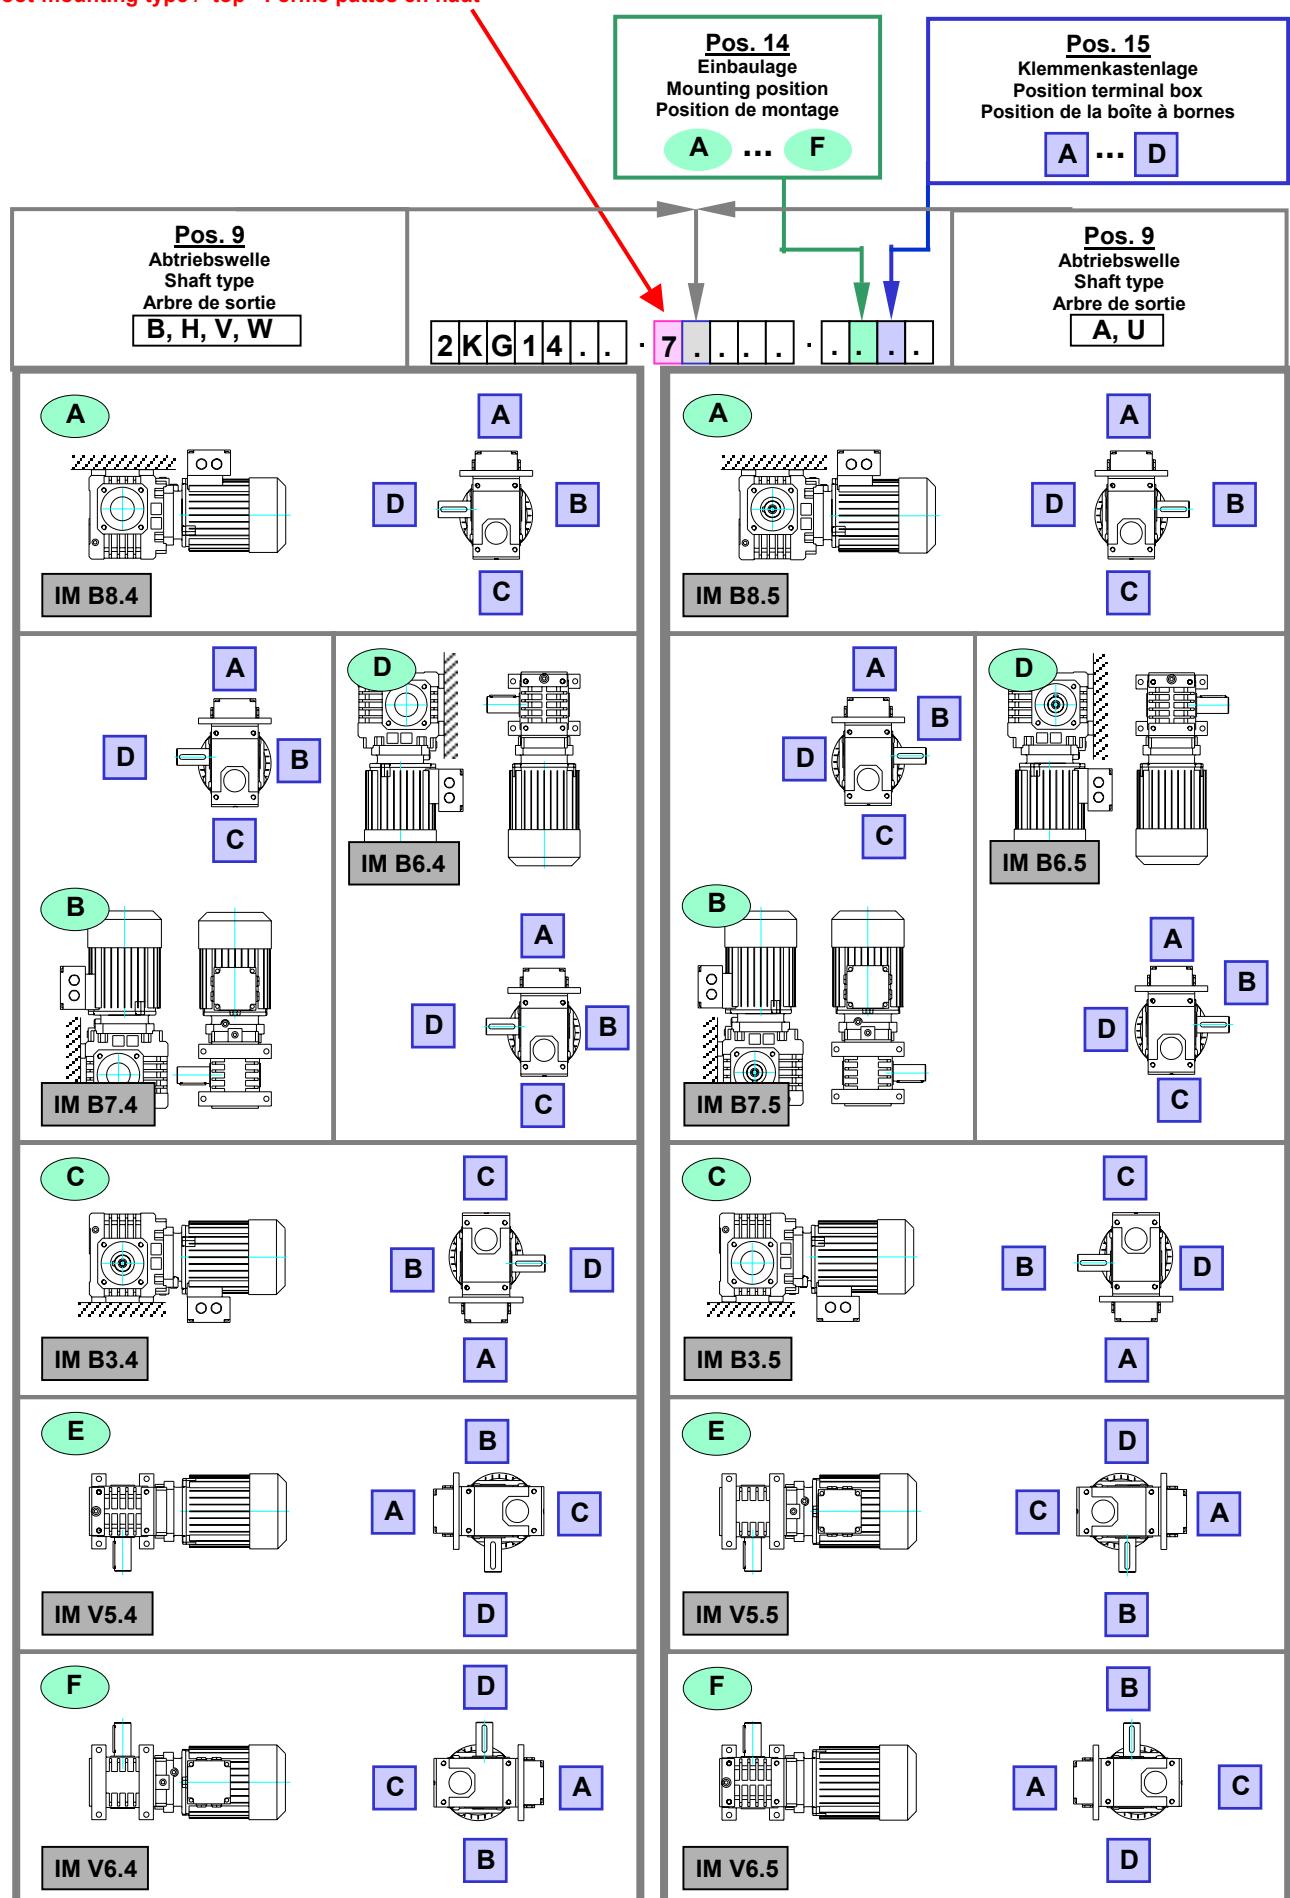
/ Fig. 4 / Tab. 4 Pos. 8 = 1 Bauform / Flansch links
